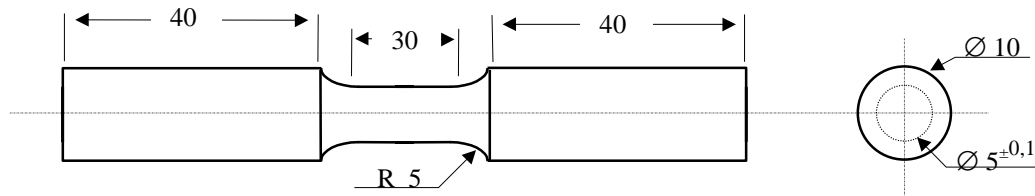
Corpo de prova de tração. Dimensões em milímetro.
